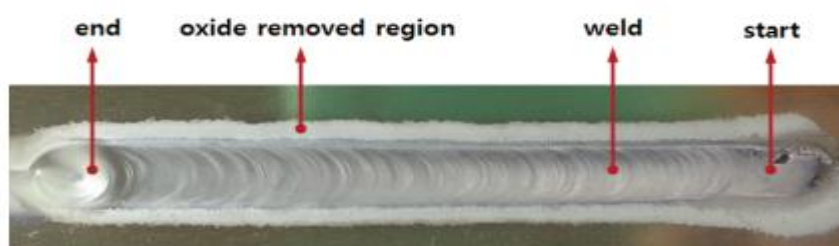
Формирование шва при сварке алюминиевого сплава 5052 [24]
